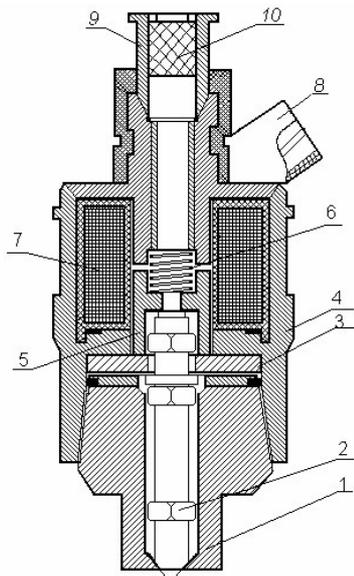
Схема ремонтпригодного инжектора, где: 1 – нижний корпус; 2 – игла; 3 – ограничительная шайба; 4 – средний корпус; 5 – сердечник; 6 – пружина; 7 – обмотка электромагнита; 8 – электрический разъем; 9 – верхний корпус; 10 – фильтр
